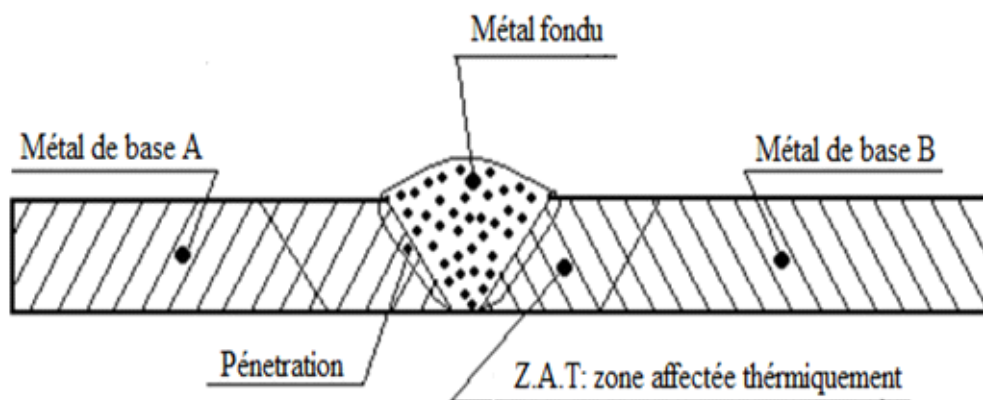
Différentes parties d'une soudure [Bill Taylor, Anne Guesnier: Métallographie des soudures].
